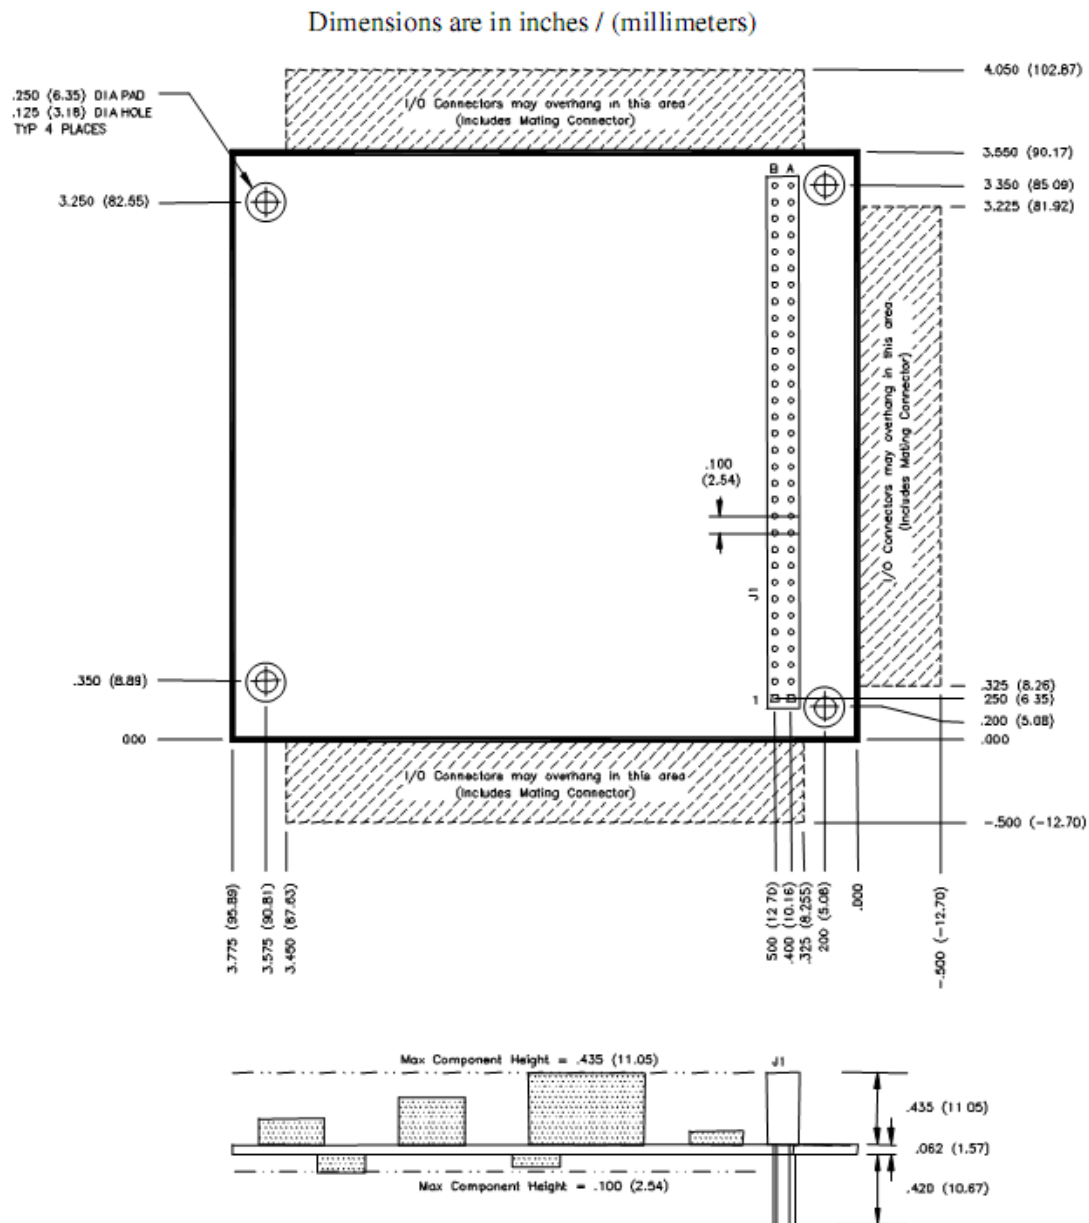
Dimensions del mòdul PC/104 8 bits
